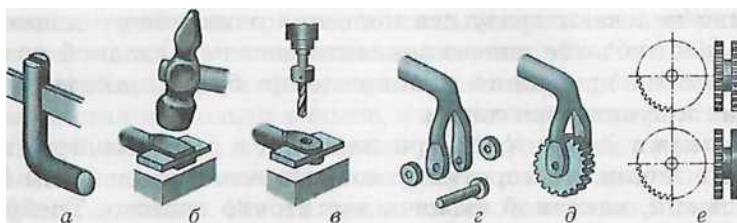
Последовательность изготовления накатки: *а* — пропиливание в стержне продольного паза; *б* — ковка; *в* — сверление отверстий; *г* — готовая вилка; *д* — готовая накатка; *е* — двоянное зубчатое колесо; двоянное зубчатое колесо с прямым диском
